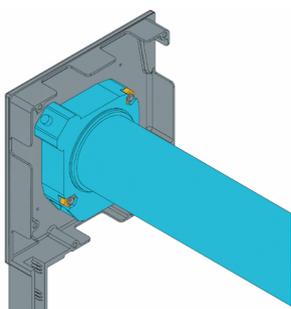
Внутривальный привод в сборе с крышкой боковой роллетной
